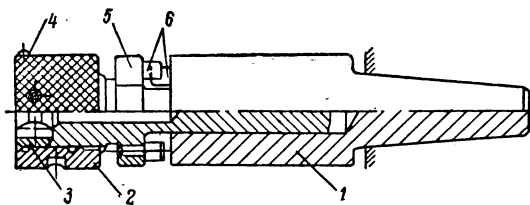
Плашкодержатель усовершенствованной конструкции.
